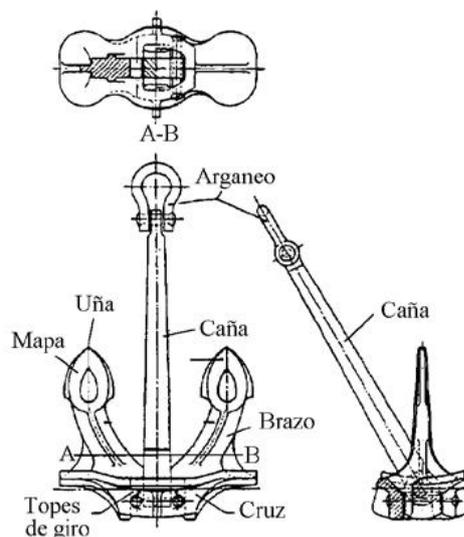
Ancla de tipo Hall. Fuente: Esteve-Pérez, J.A (s.f.). Construcción Naval
